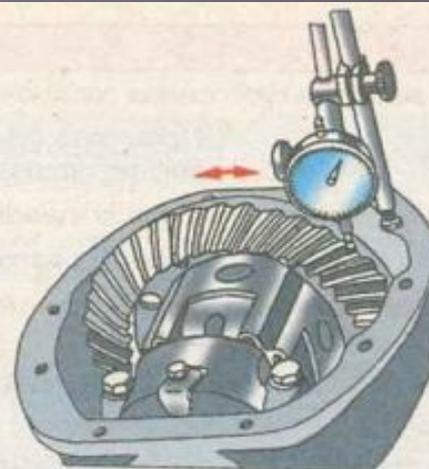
Проверка бокового зазора в зацеплении зубьев шестерен главной передачи (неразъемный задний мост)
